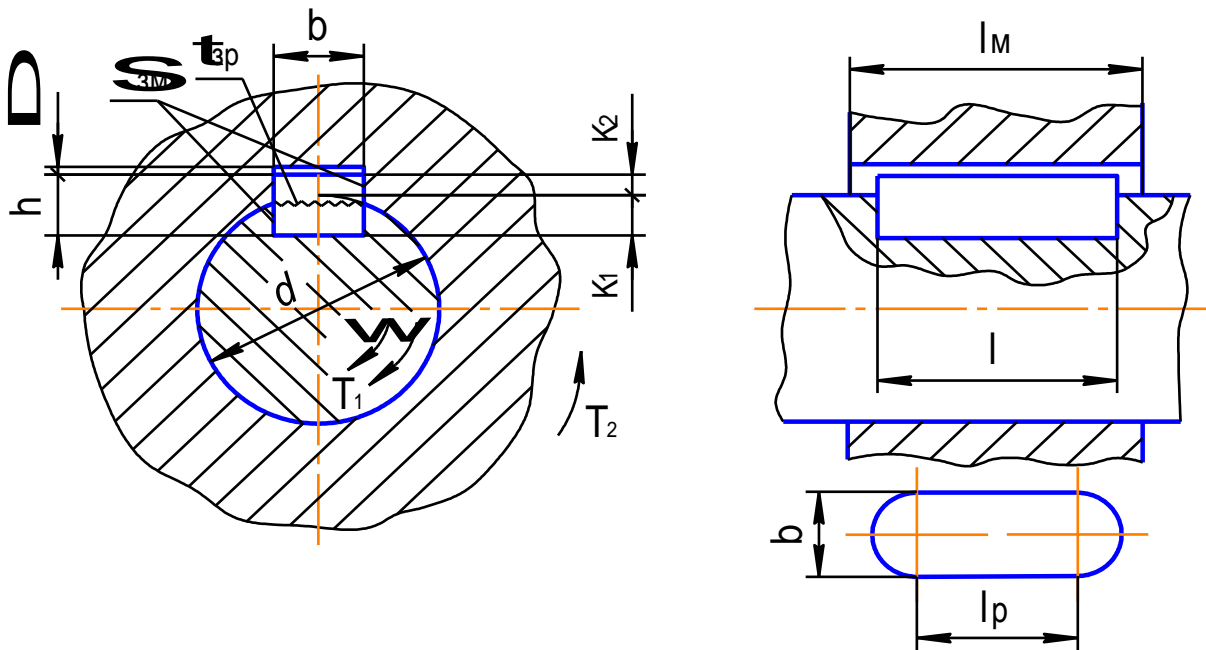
Конструкція шпонкового з'єднання з призматичною шпонкою
